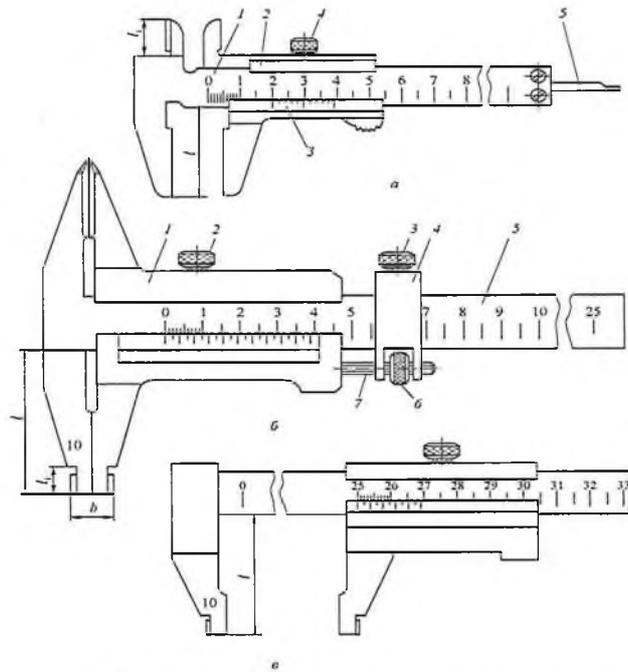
Общий вид штангенциркуля ШЦ-1
